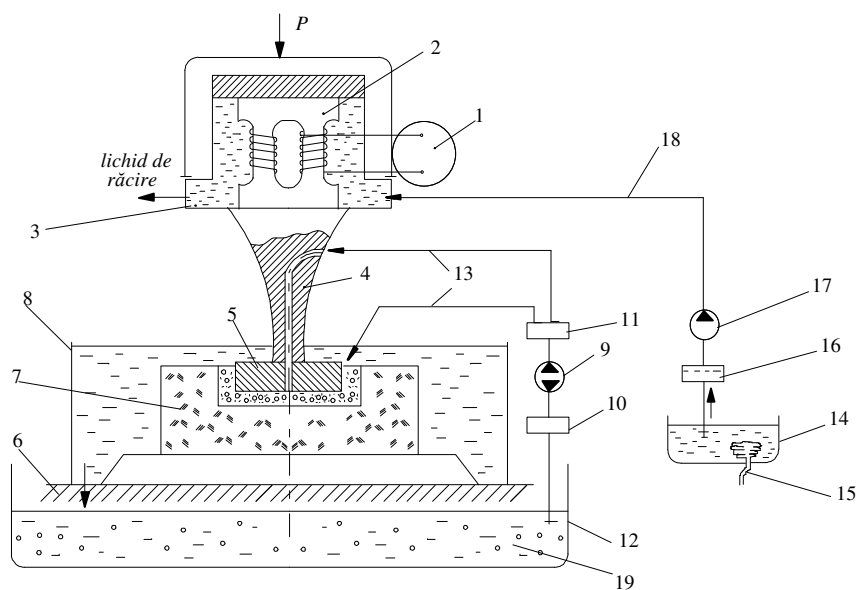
Schema de principiu a unei instalații de prelucrare dimensională cu ultrasunete:
